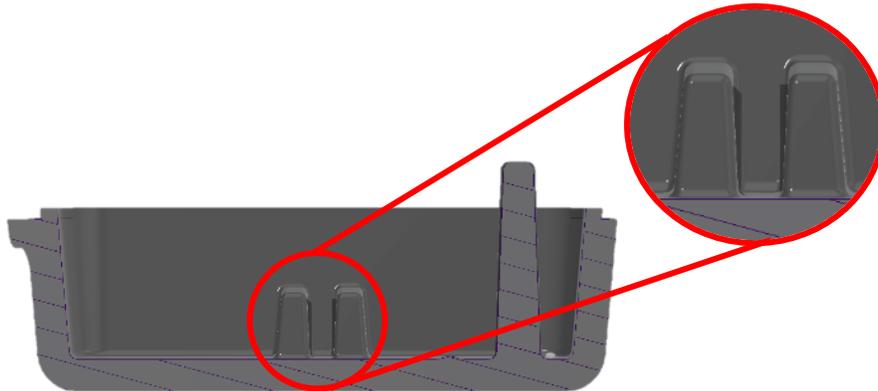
Vista lateral seccionada (Propuesta 5).
